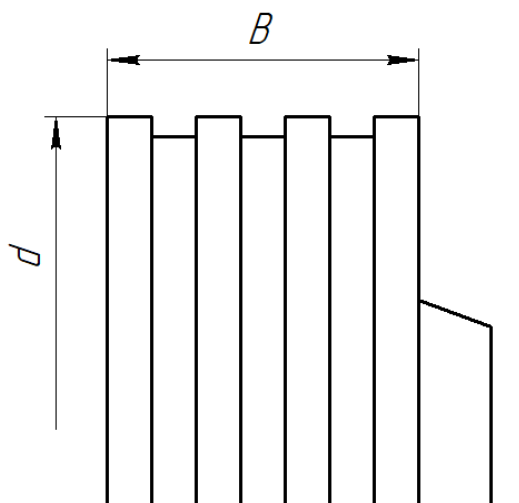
Шкив цилиндрической формы с кольцевыми канавками
